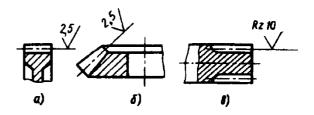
Обозначение шероховатости поверхности зубъев детали без указания их профиля
